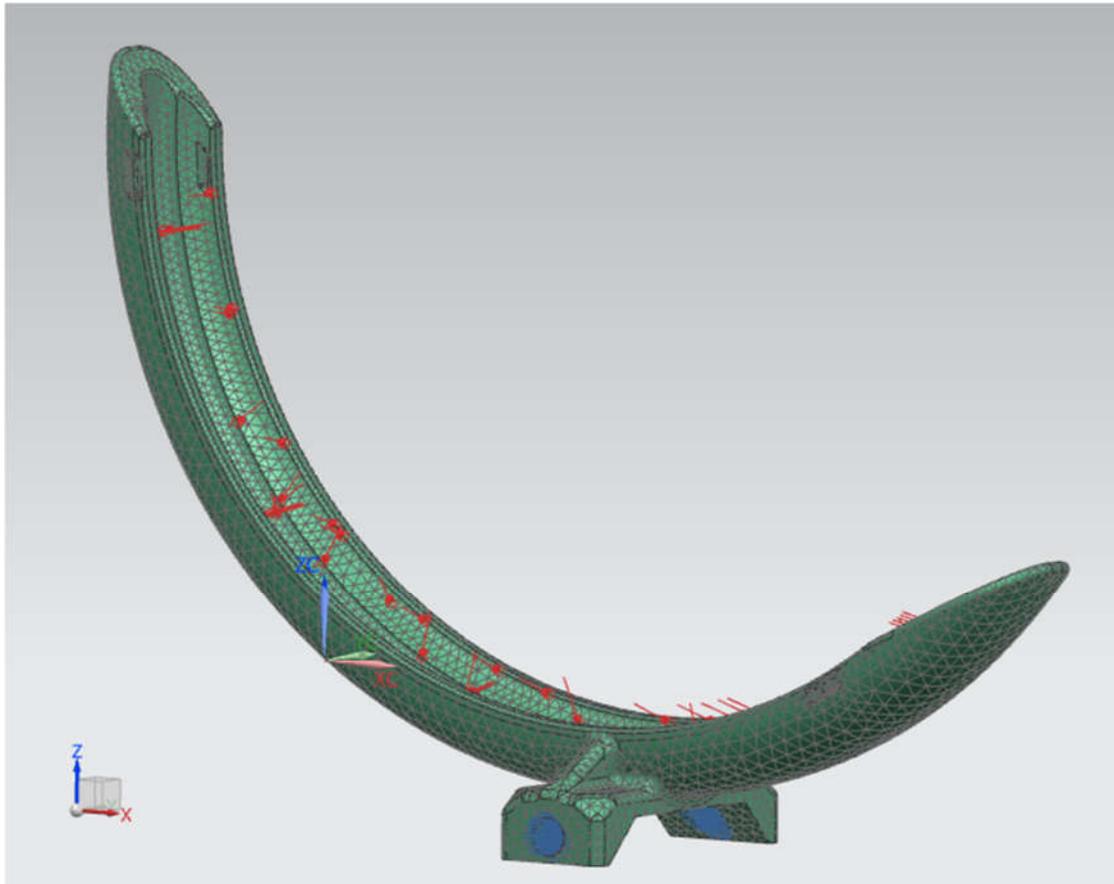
Mallado, restricciones y fuerzas del elemento 1.1.2/2.1.1
